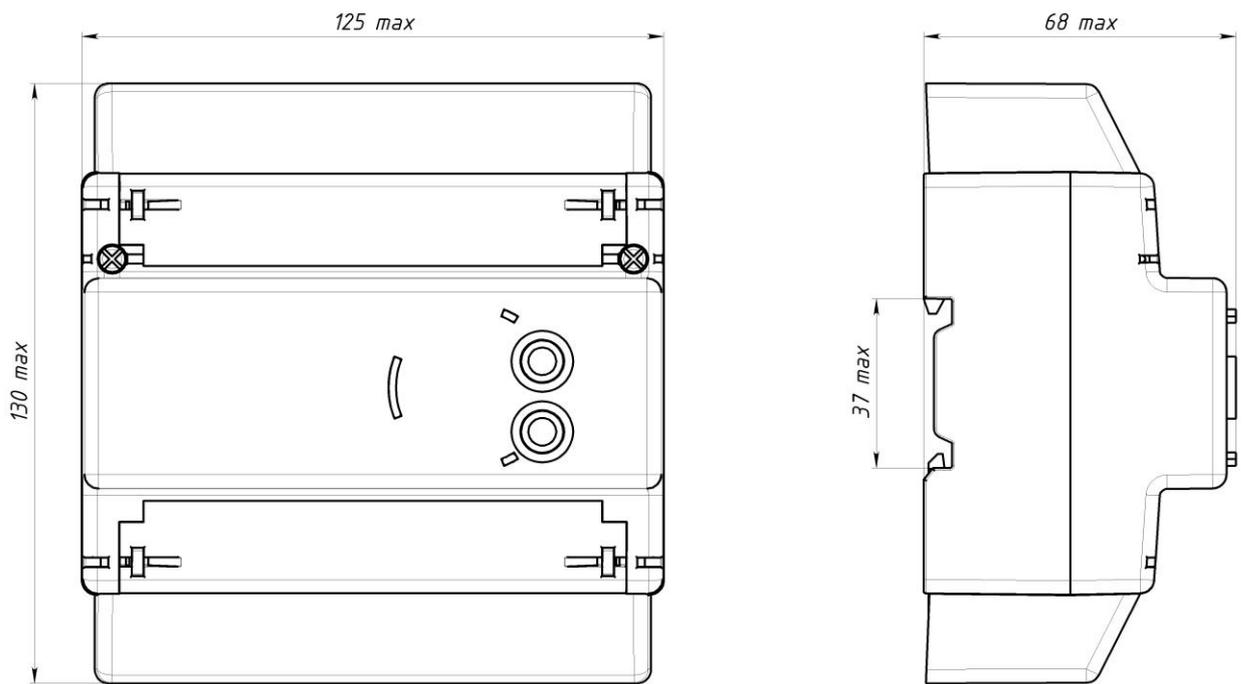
б – Корпус 7мТН35 со стандартными клеммными крышками
